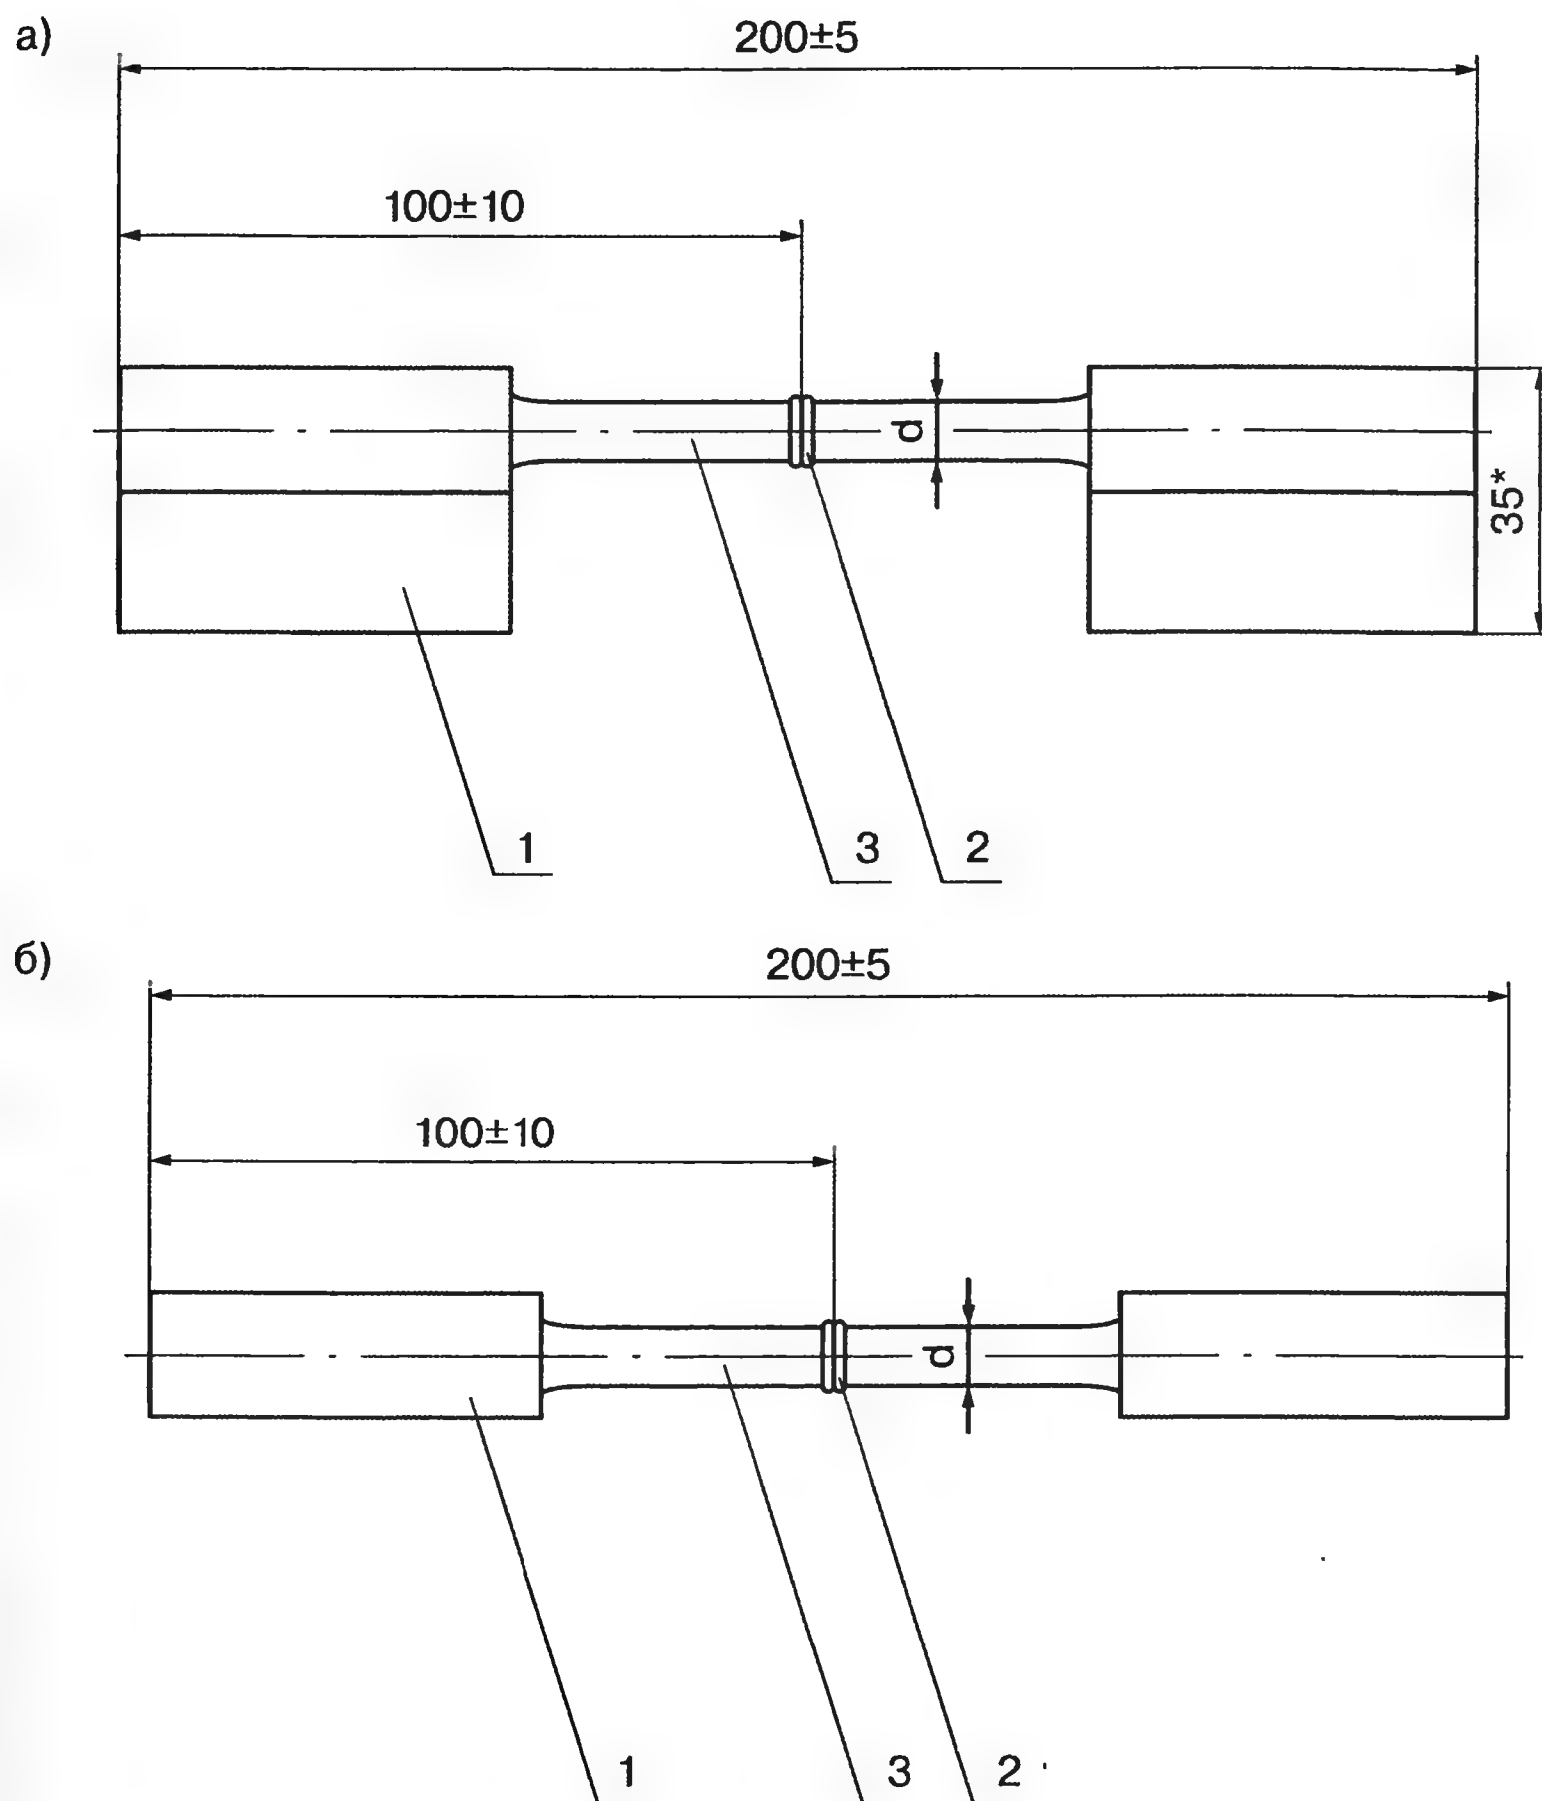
Соединитель а) фартучный; б) бесфартучный рельсовый стыковой приварной СРФ, где: 1 — манжета; 2 — проволока; 3 — провод
